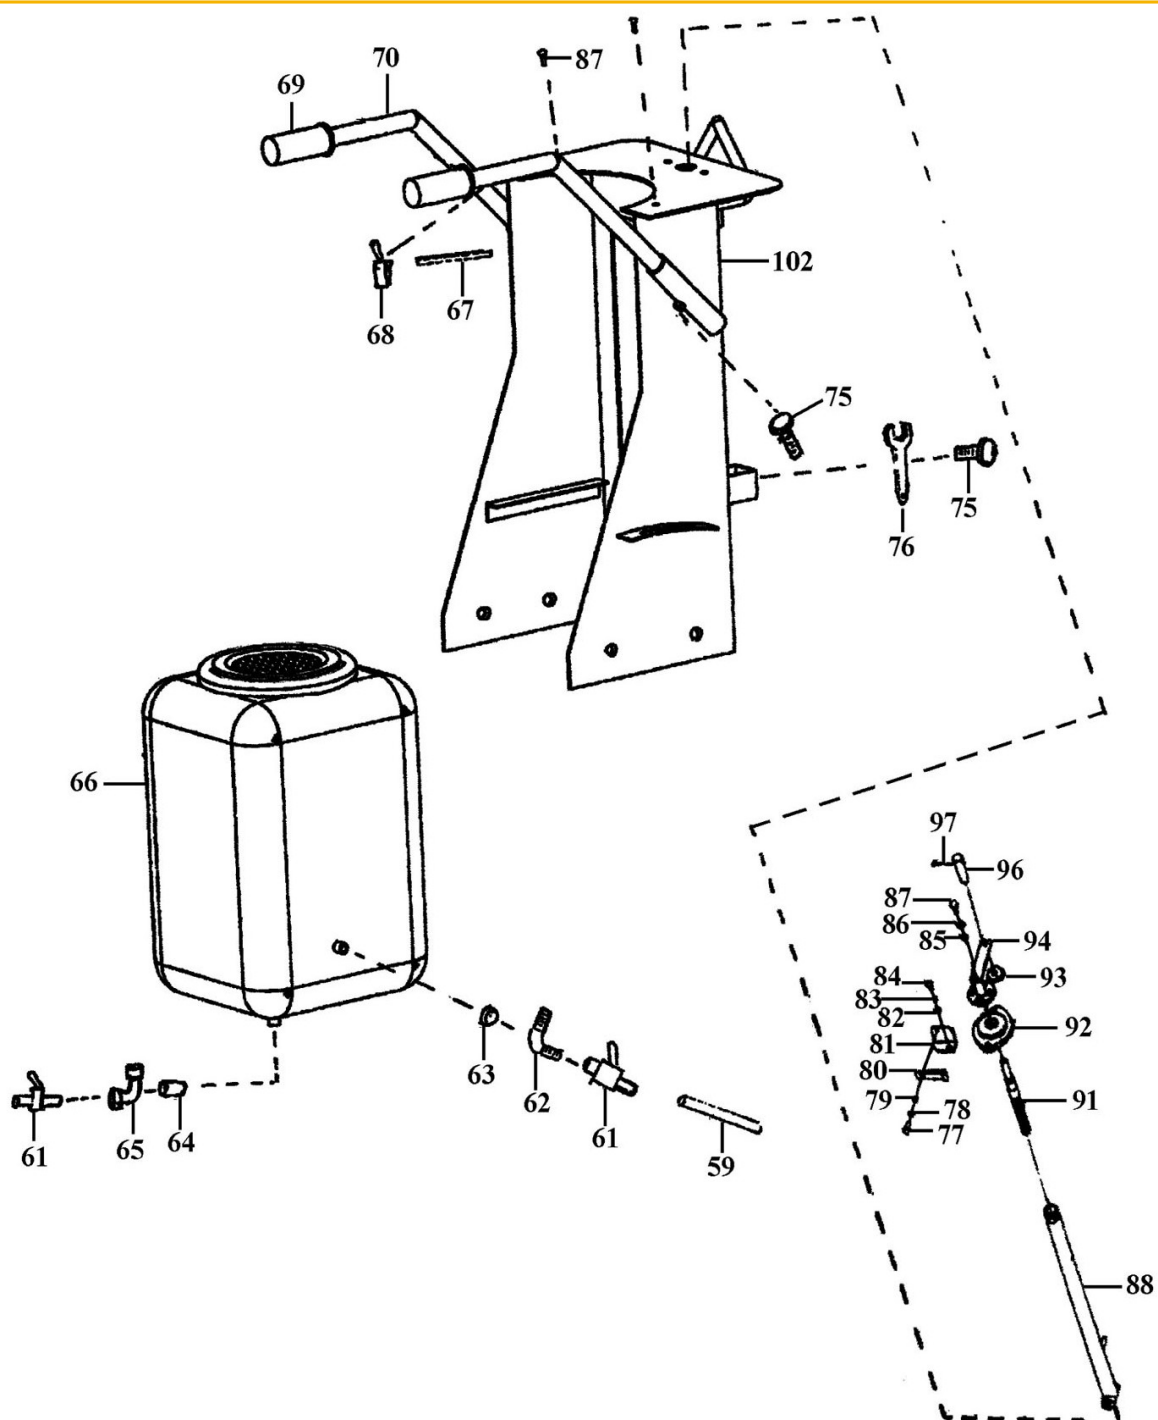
Vista explodida: depósito de água, guiador e mecanismo de elevação
